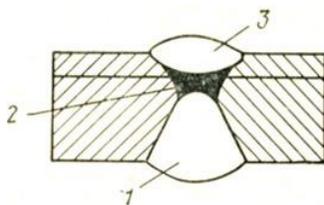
Сварка двухслойной стали с разделительным слоем 1 - слой со стороны основного металла; 2 - разделительный слой; 3 - слой со стороны облицовочного металла
